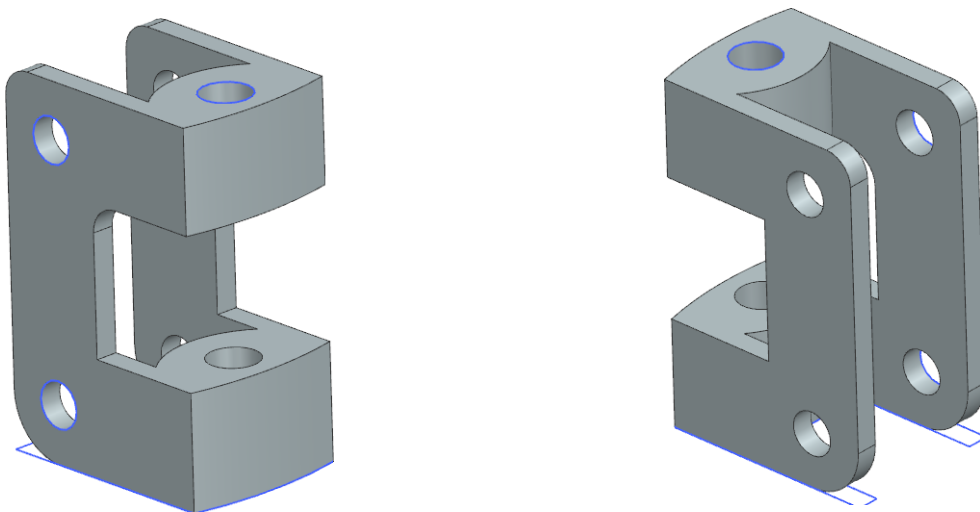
y 50. Diseño en CAD del diseño del tocho.
